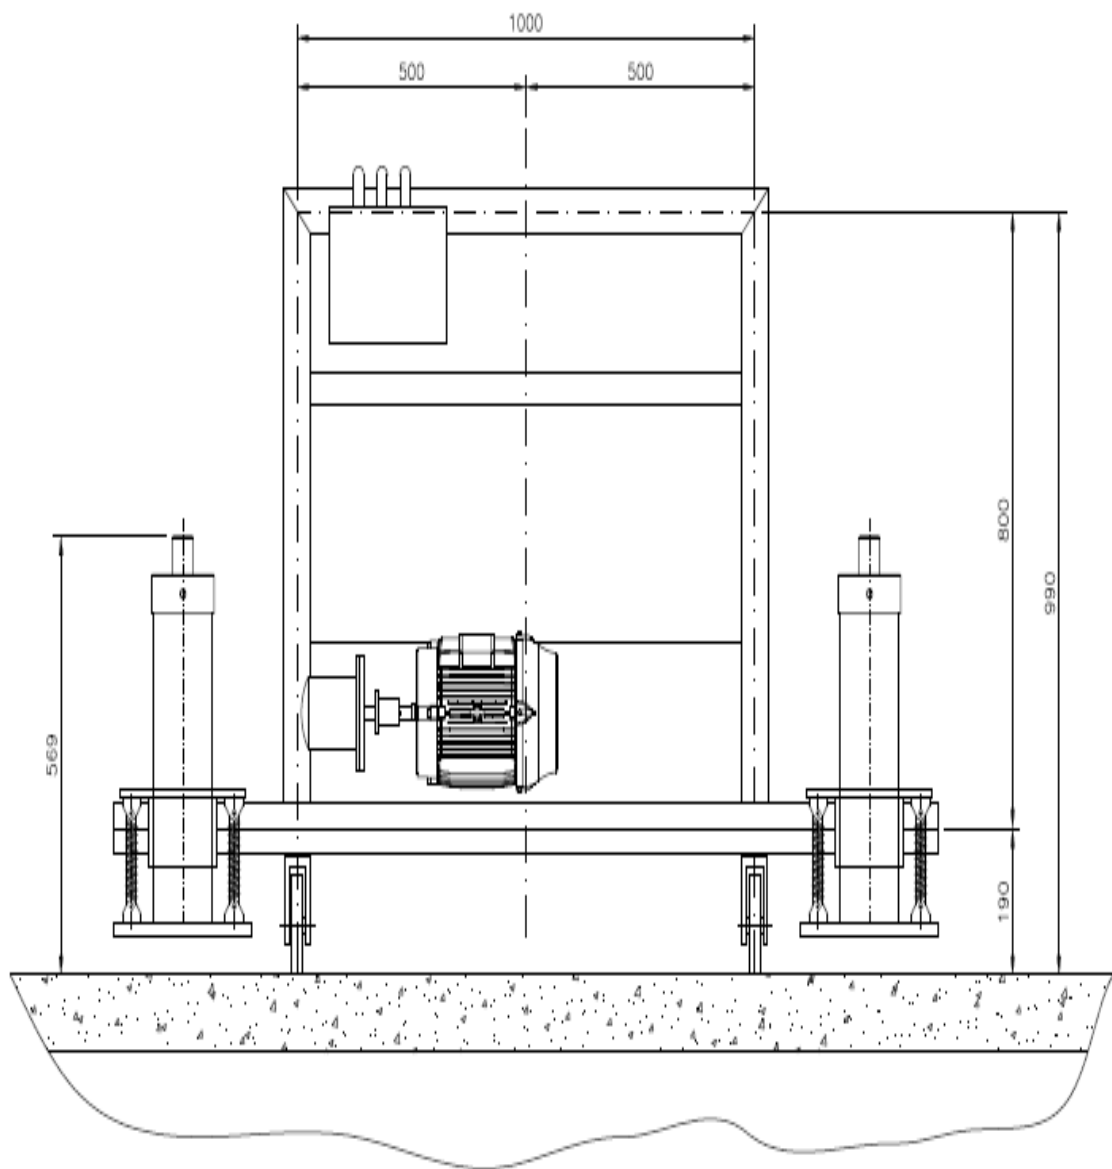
Dispositivo para Elevação, Vista Frontal. Escala 1:5, 2014.
